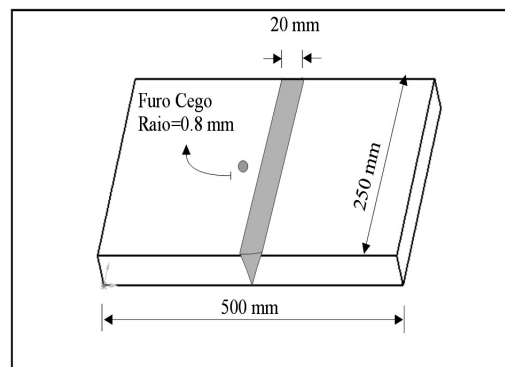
Esquema do corpo de prova soldado com furo cego
